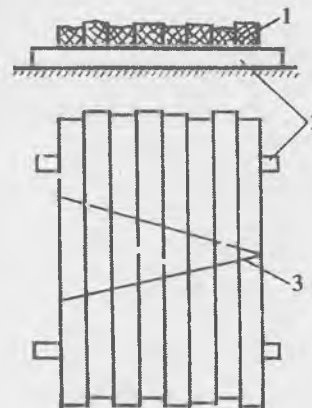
Подбор и разметка заготовок при склеивании по ширине:
